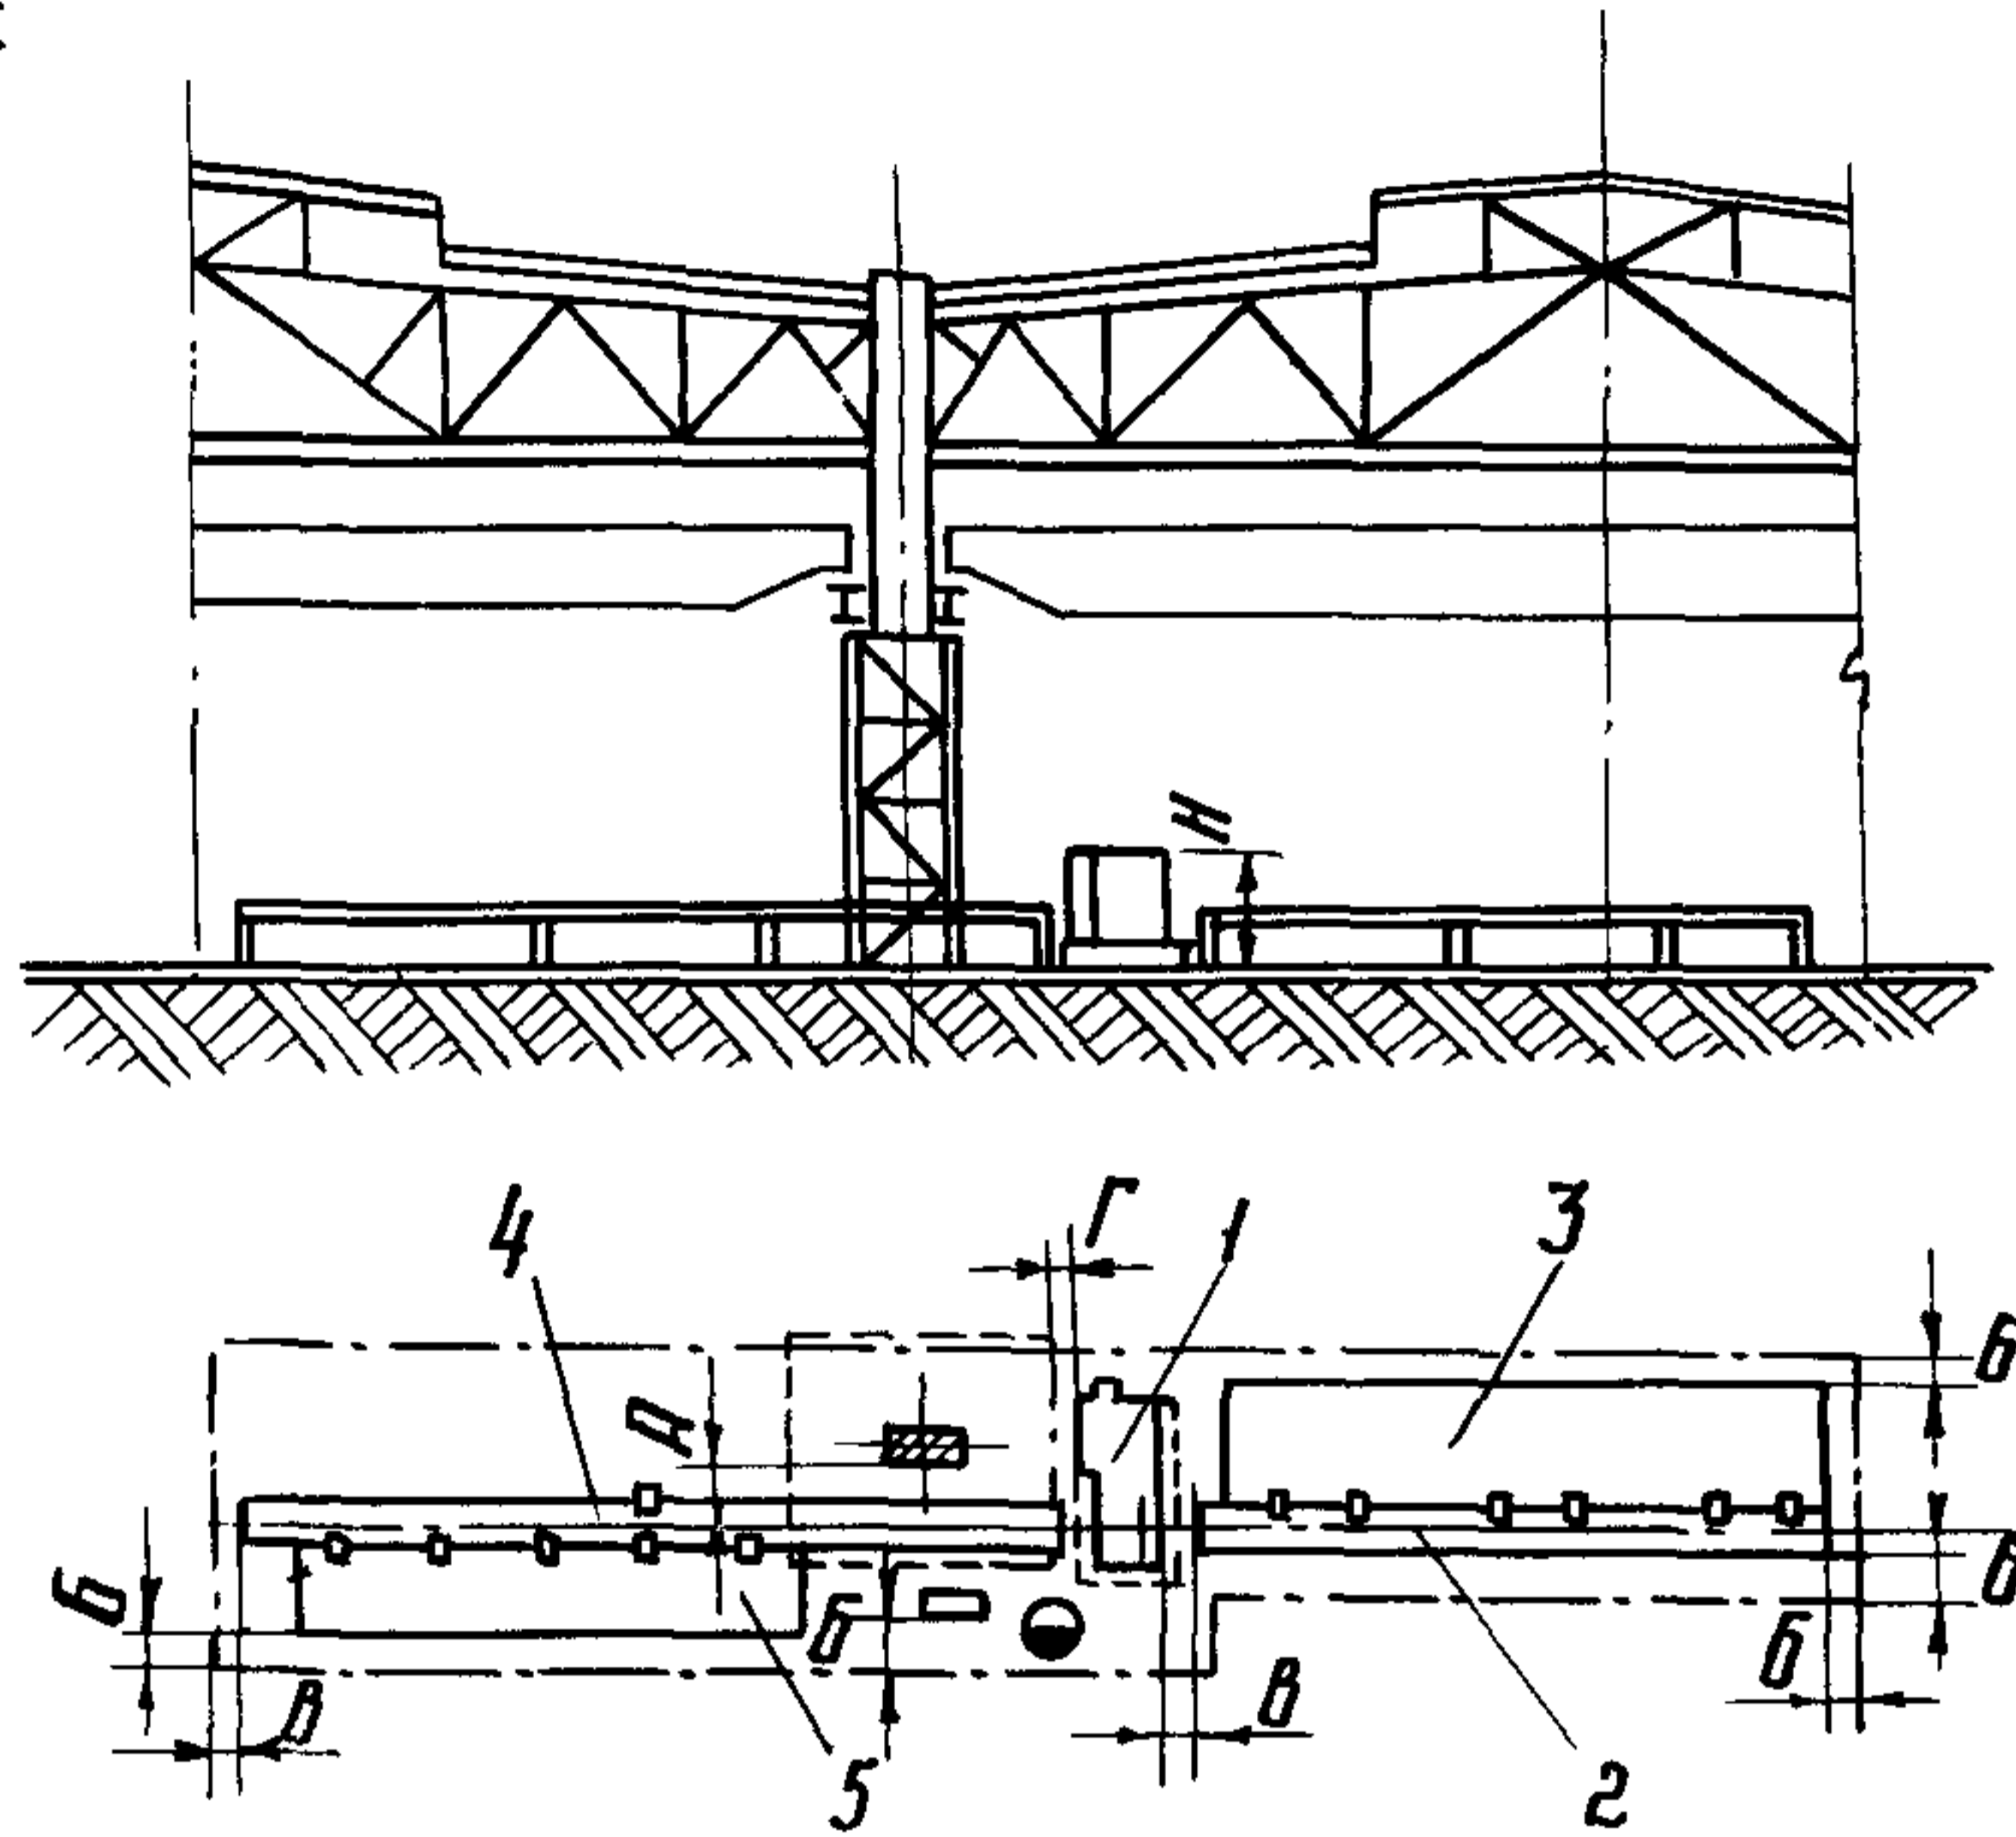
Размещение фрезерно-отрезного станка для резки балок:
